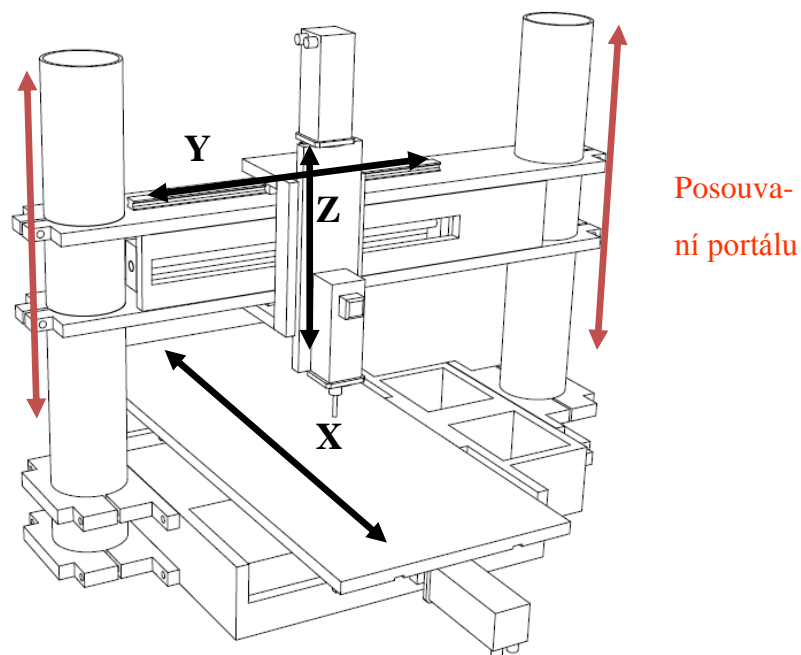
Prvotní návrh originální konstrukce 3 osé CNC frézky.
